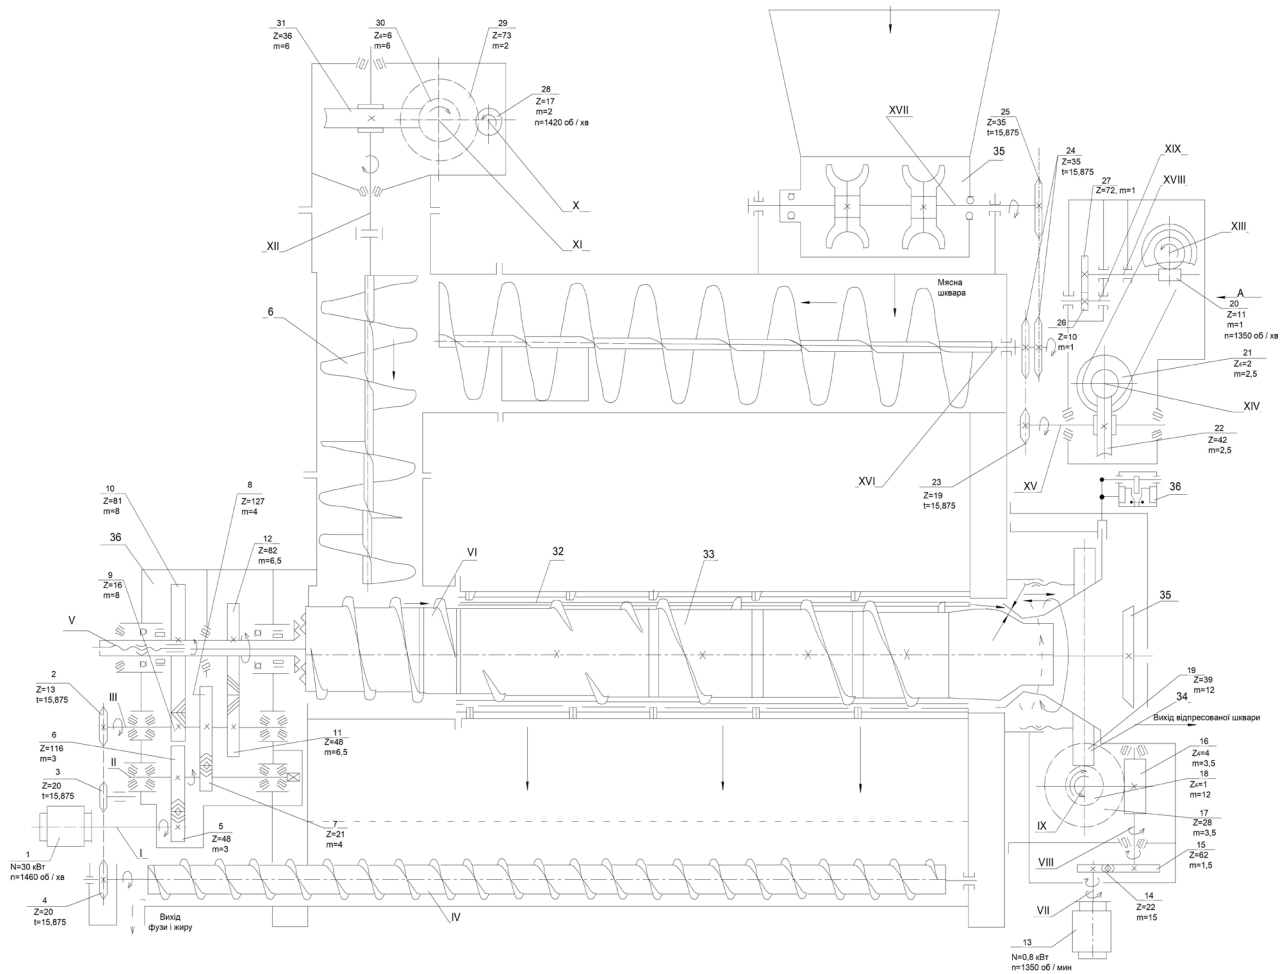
Кінематична схема преса Е8-ФОБ
